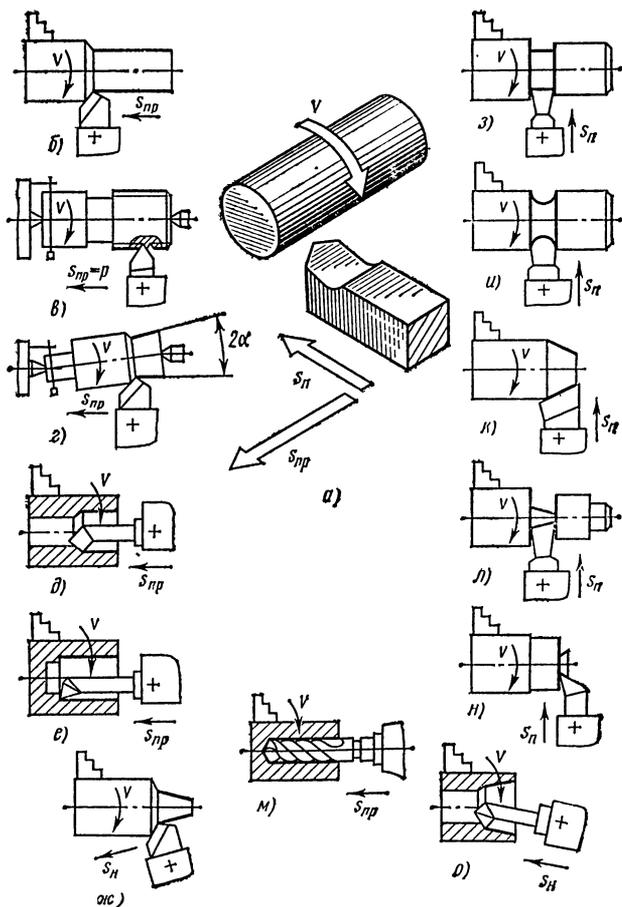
Схемы обработки поверхностей заготовок на токарно-винторезном станке
